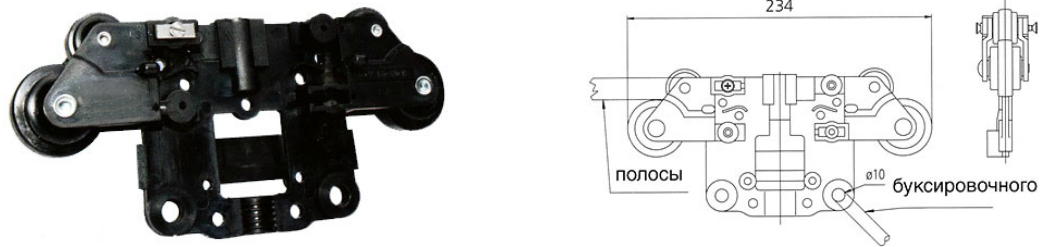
Общий вид каретки для протяжки медной полосы.
